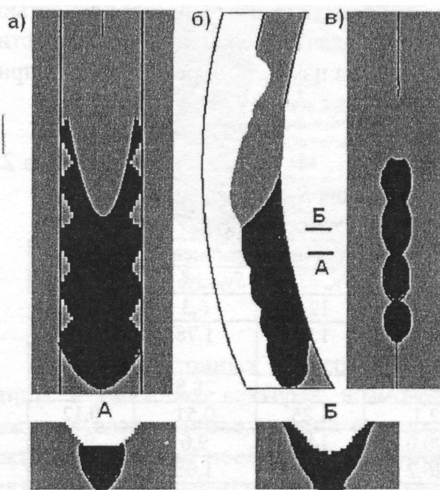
Форма сварочной ванны и шва при сварке в положениях 11-1 ч и 7-8 ч: а) внешняя поверхность трубы, б) плоскость стыка, в) внутренняя поверхность шва, А, Б — сечения шва в паузе и импульсе тока
